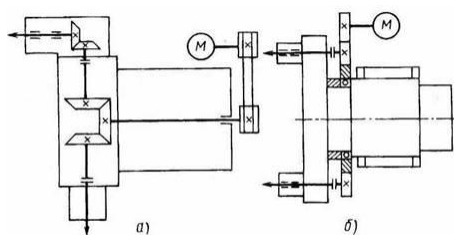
Револьверные головки токарных модулей с вращающимся инструментом:
